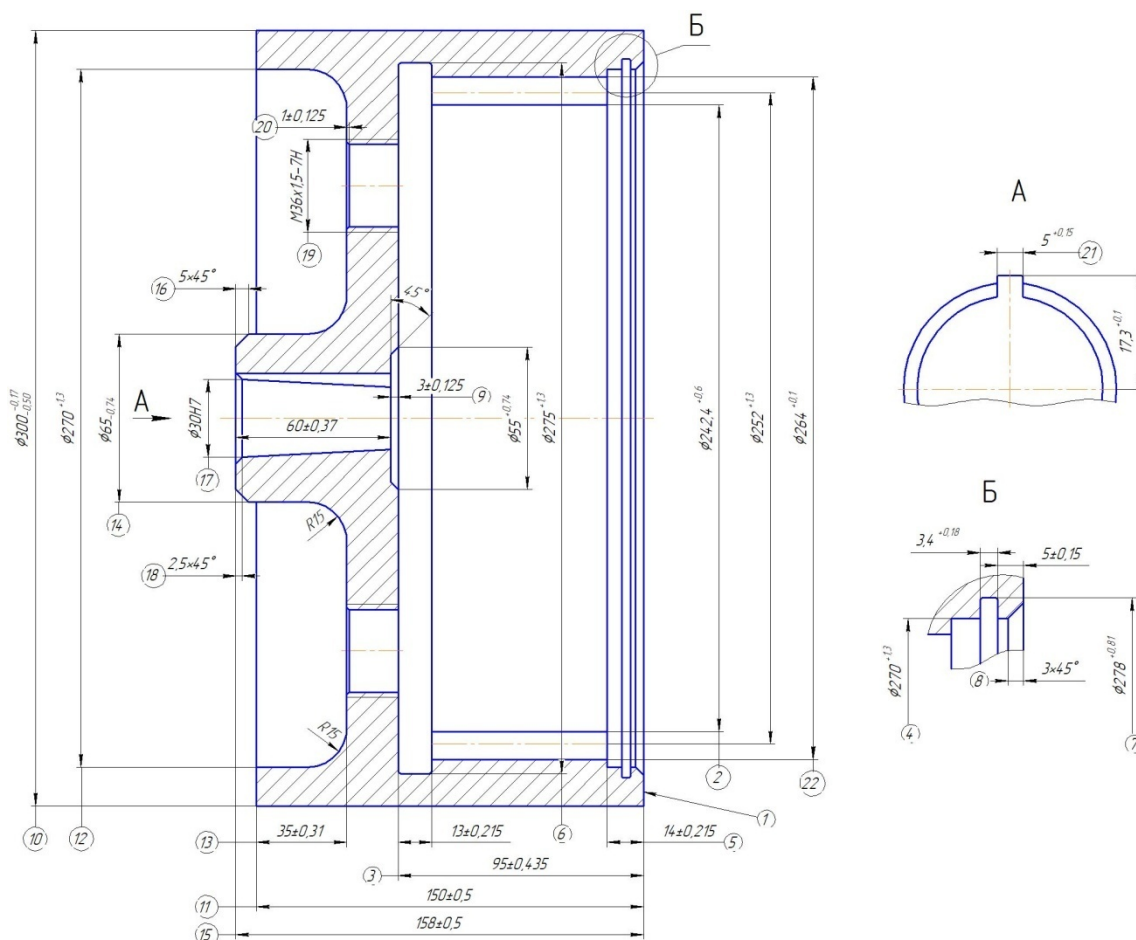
Обрабатываемые поверхности детали "Корпус муфты"
